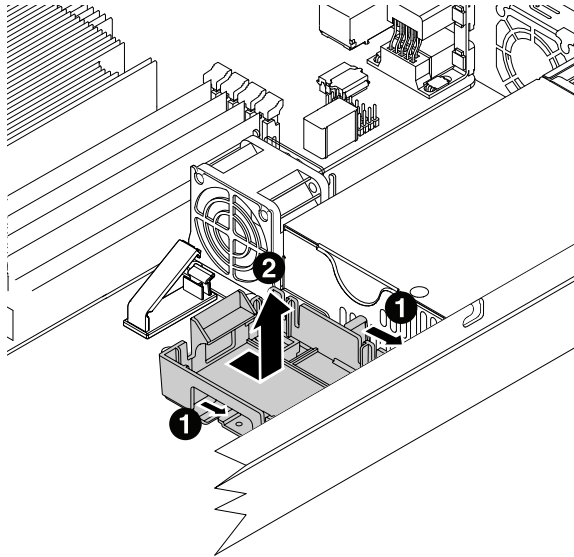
Halterung für ThinkServer RAID Super Capacitor Module aus dem Gehäuse entfernen
